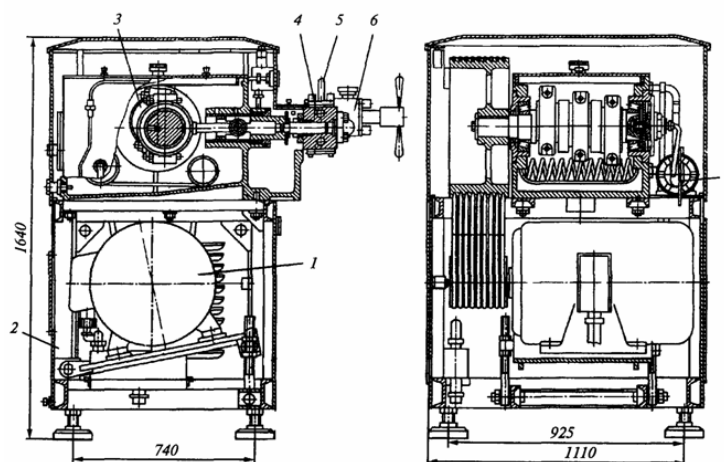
Гомогенізатор А1-ОГМ: 1 – електродвигун; 2 – корпус; 3 – кривошипно-шатунний механізм; 4 – плунжерний блок; 5 – манометрична головка; 6 – гомогенізуюча головка; 7 – система змащення
